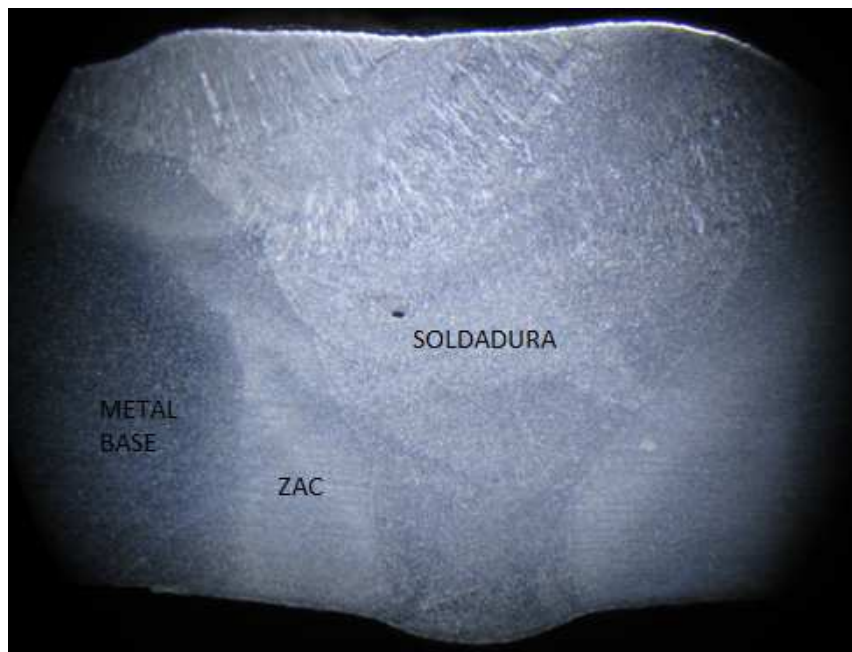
Zonas constitutivas de la junta de Soldadura (10x)
